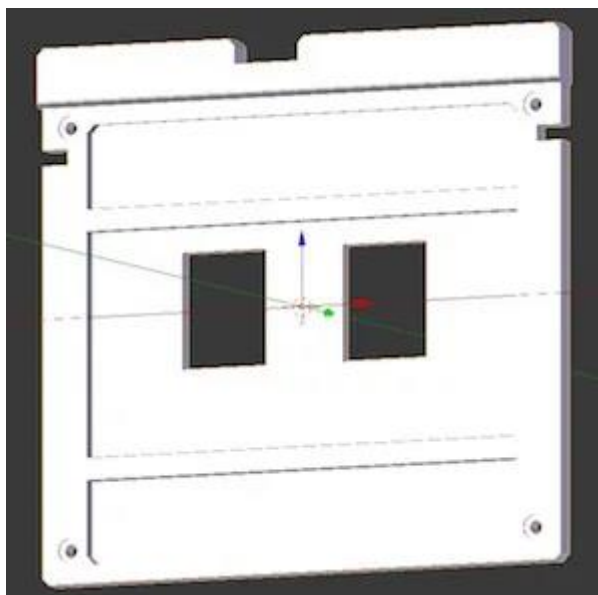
3D-модель панели кнопок в Blender button panel 3D print
